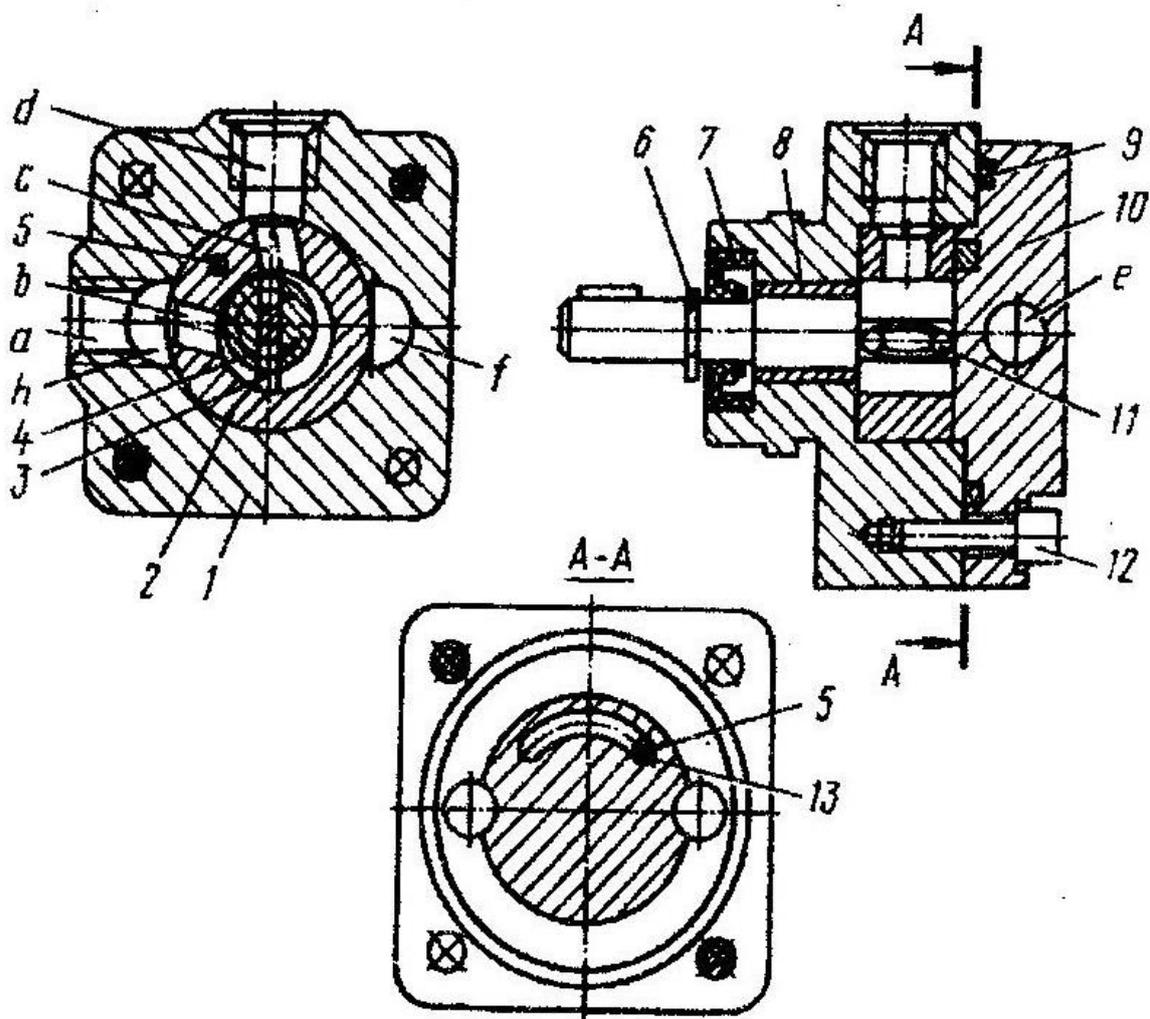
Насос пластинчатый реверсивный для смазки СИ2-4М:
